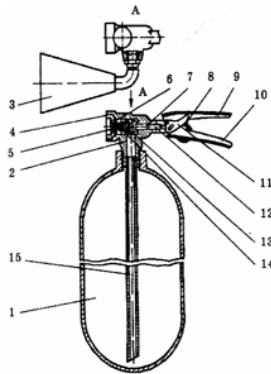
Вогнегасники вуглекислотні ОУ-2 та ОУ-5: 1 - корпус; 2 - головка; 3 - розпилювач; 4 - гайка; 5 - запобіжна мембрана; 6 - шайба; 7 - кільце ущільнювача; 8 - запобіжна частина; 9 - важіль керування клапаном; 10 - ручка; 11 - кулачок; 12 - шток; 13 - клапан; 14 - пружина; 15 - трубка сифона.
